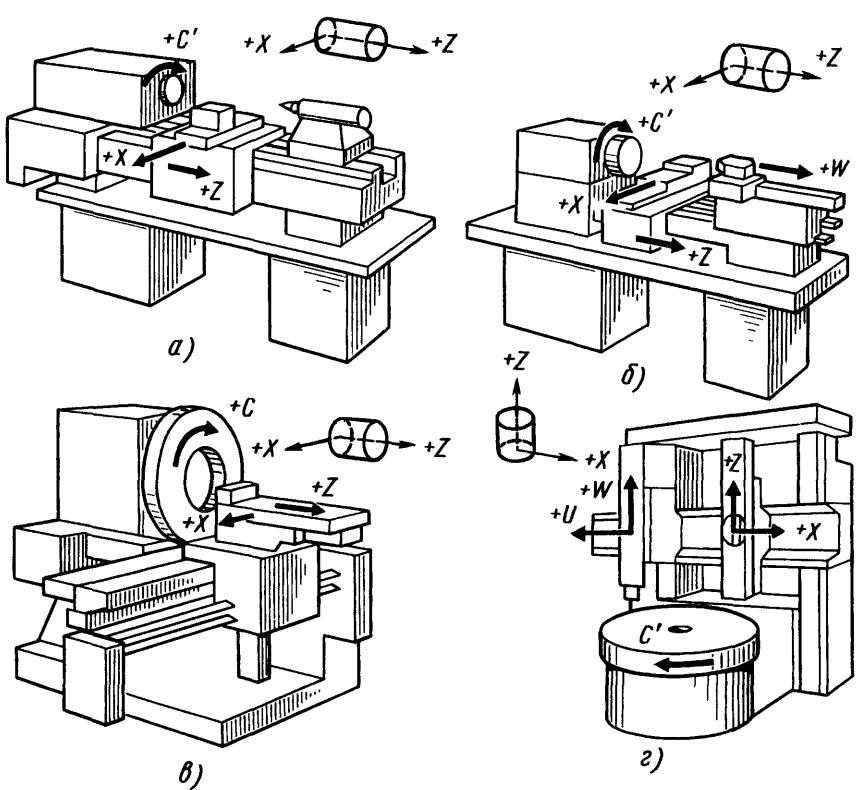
Обозначение осей координат и положительных направлений движения в токарных станках с ЧПУ:
